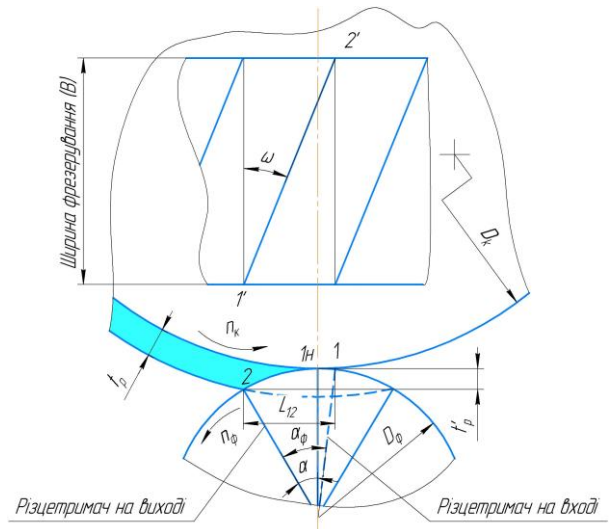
Розрахункова схема умови рівномірного фрезерування колісної пари
